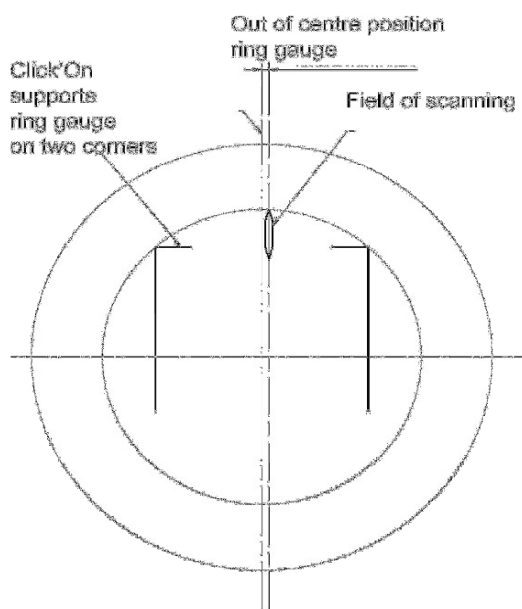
Промежуточная калибровка поддержки с калиброванными установочными кольцами
